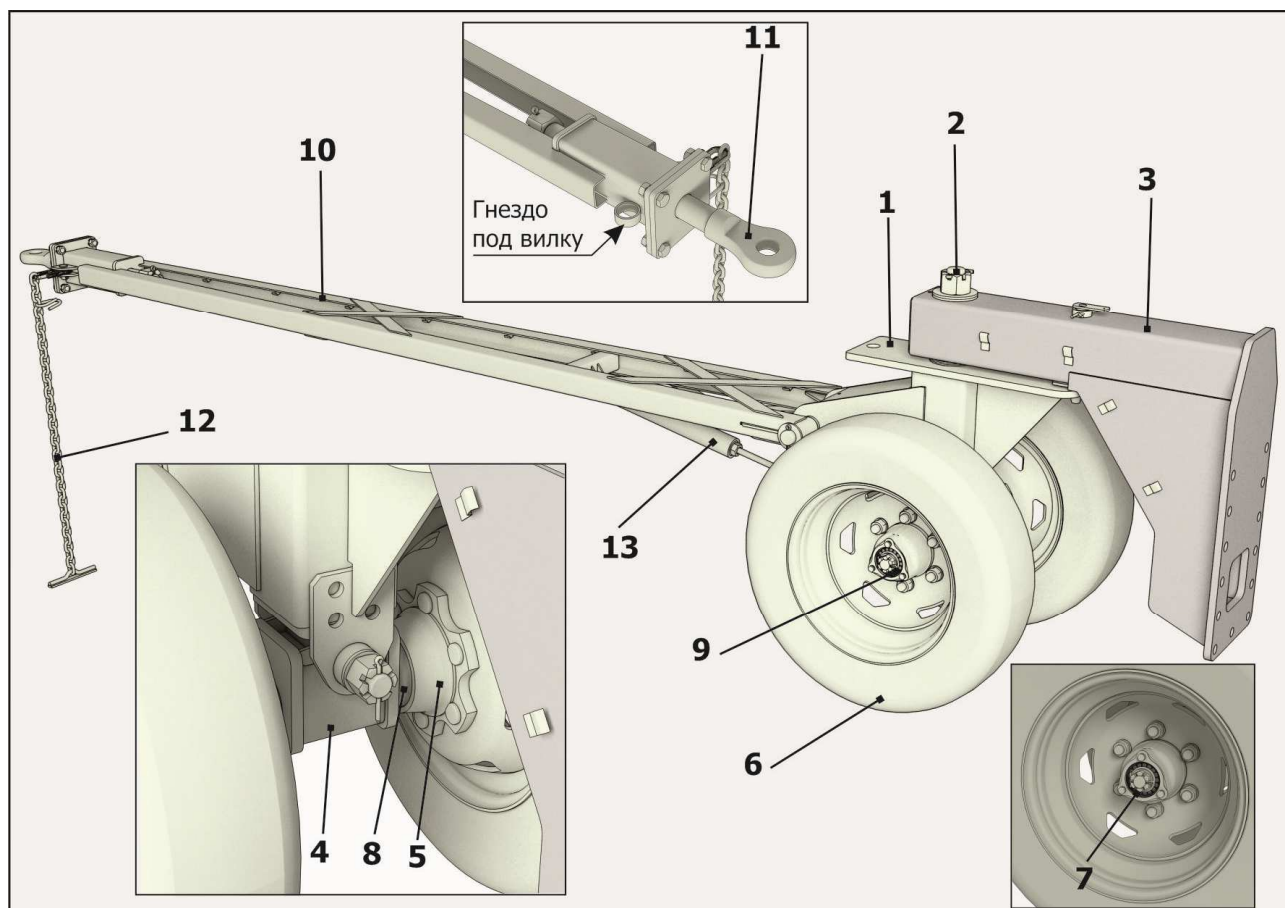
Общий вид приспособления для перемещения адаптеров
